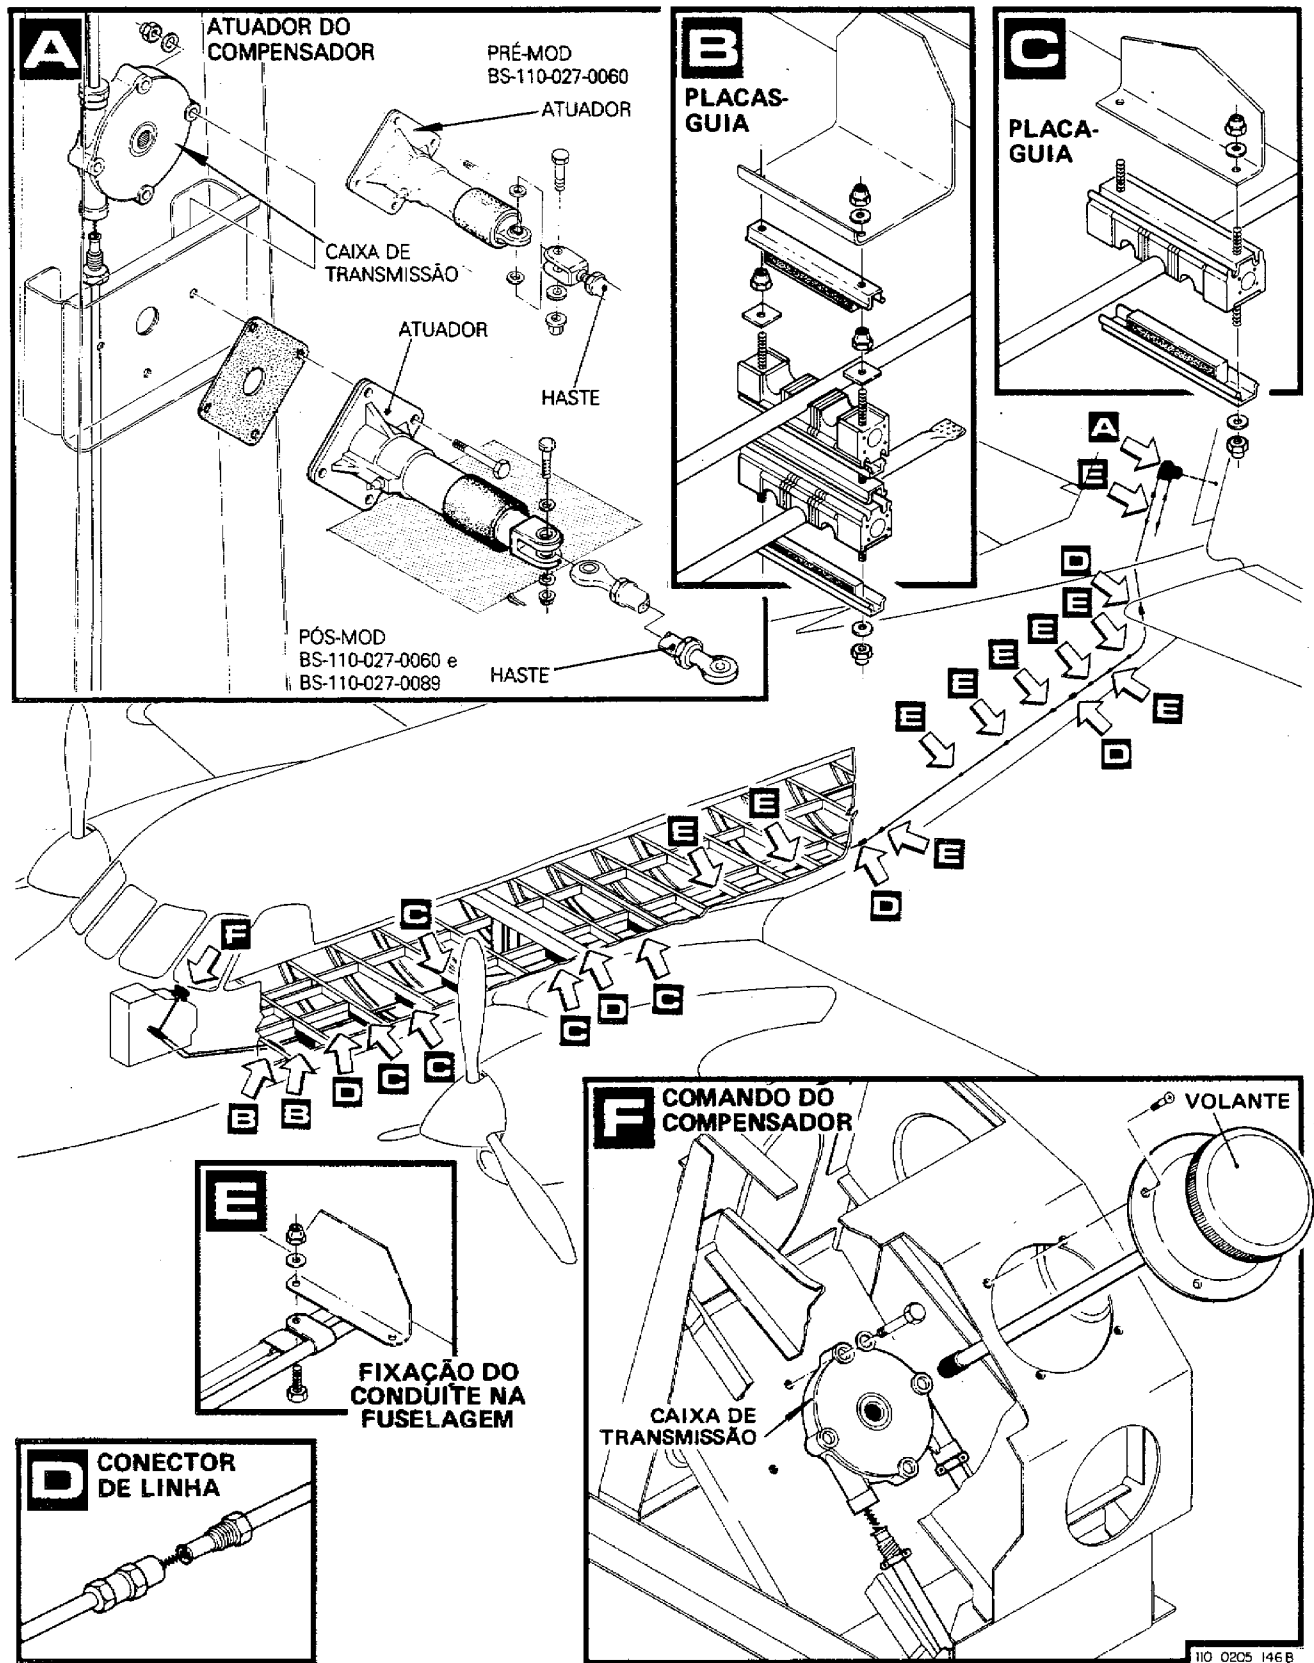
Remoção/Instalação do Sistema de Comando do Compensador do Leme de Direção
